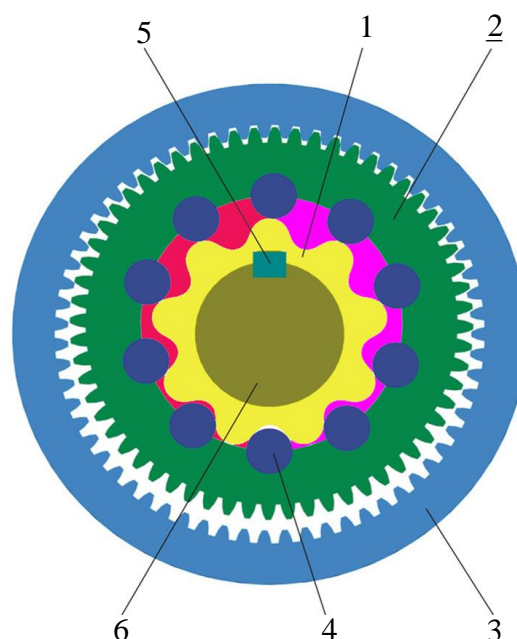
Компенсація планетарного руху роторів за допомогою зовнішнього зубчастого зачеплення: 1 – внутрішній ротор (сонячна шестерня); 2 – зовнішній ротор (сателіт); 3 – корпус (коронна шестерня); 4 – ролик; 5 – шпонка; 6 - вал
